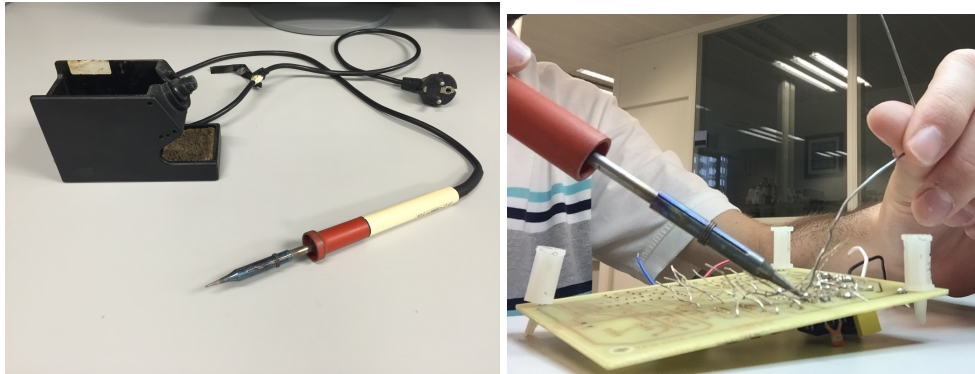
Soldador de 26 vatios de potencia. / Proceso de soldadura
